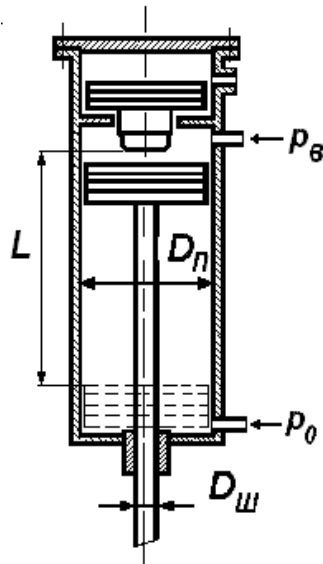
Схема рабочего цилиндра и предохранителя паровоздушного молота
